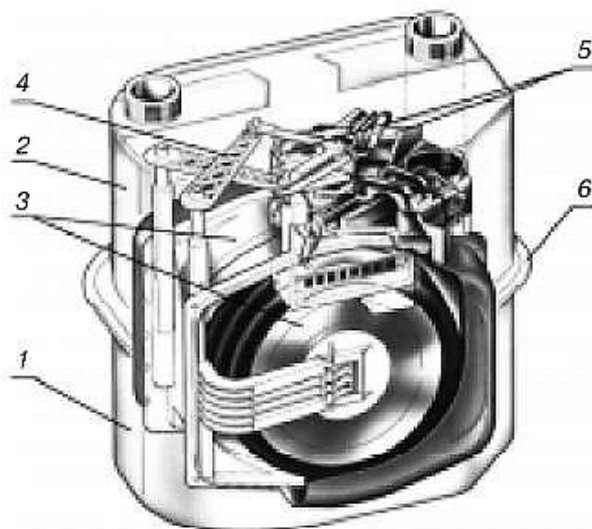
Диафрагменный счетчик: 1 — корпус; 2 — крышка; 3 — измерительный механизм; 4 — кривошипно-рычажной механизм; 5 — верхние клапаны газораспределительного устройства; 6 — стяжная полоса.
